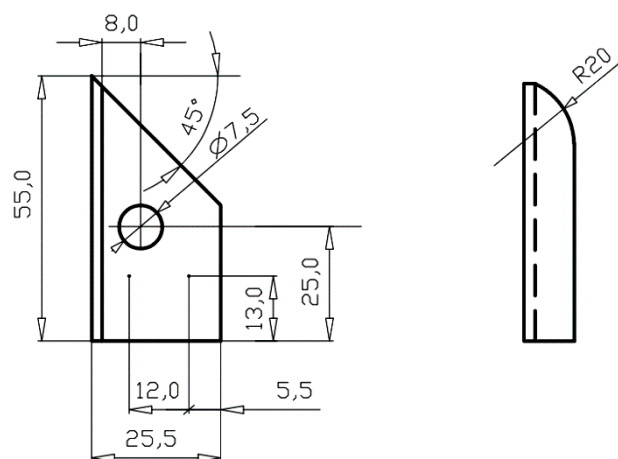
Конструктивное решение и гарбаритные размеры зажима флексометра
